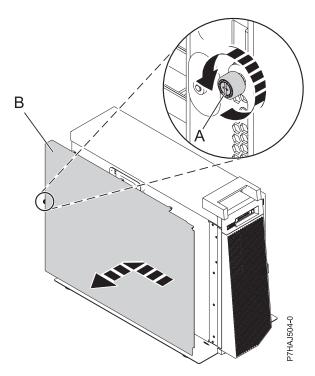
Instalando a Tampa Externa de Acesso de Serviço
